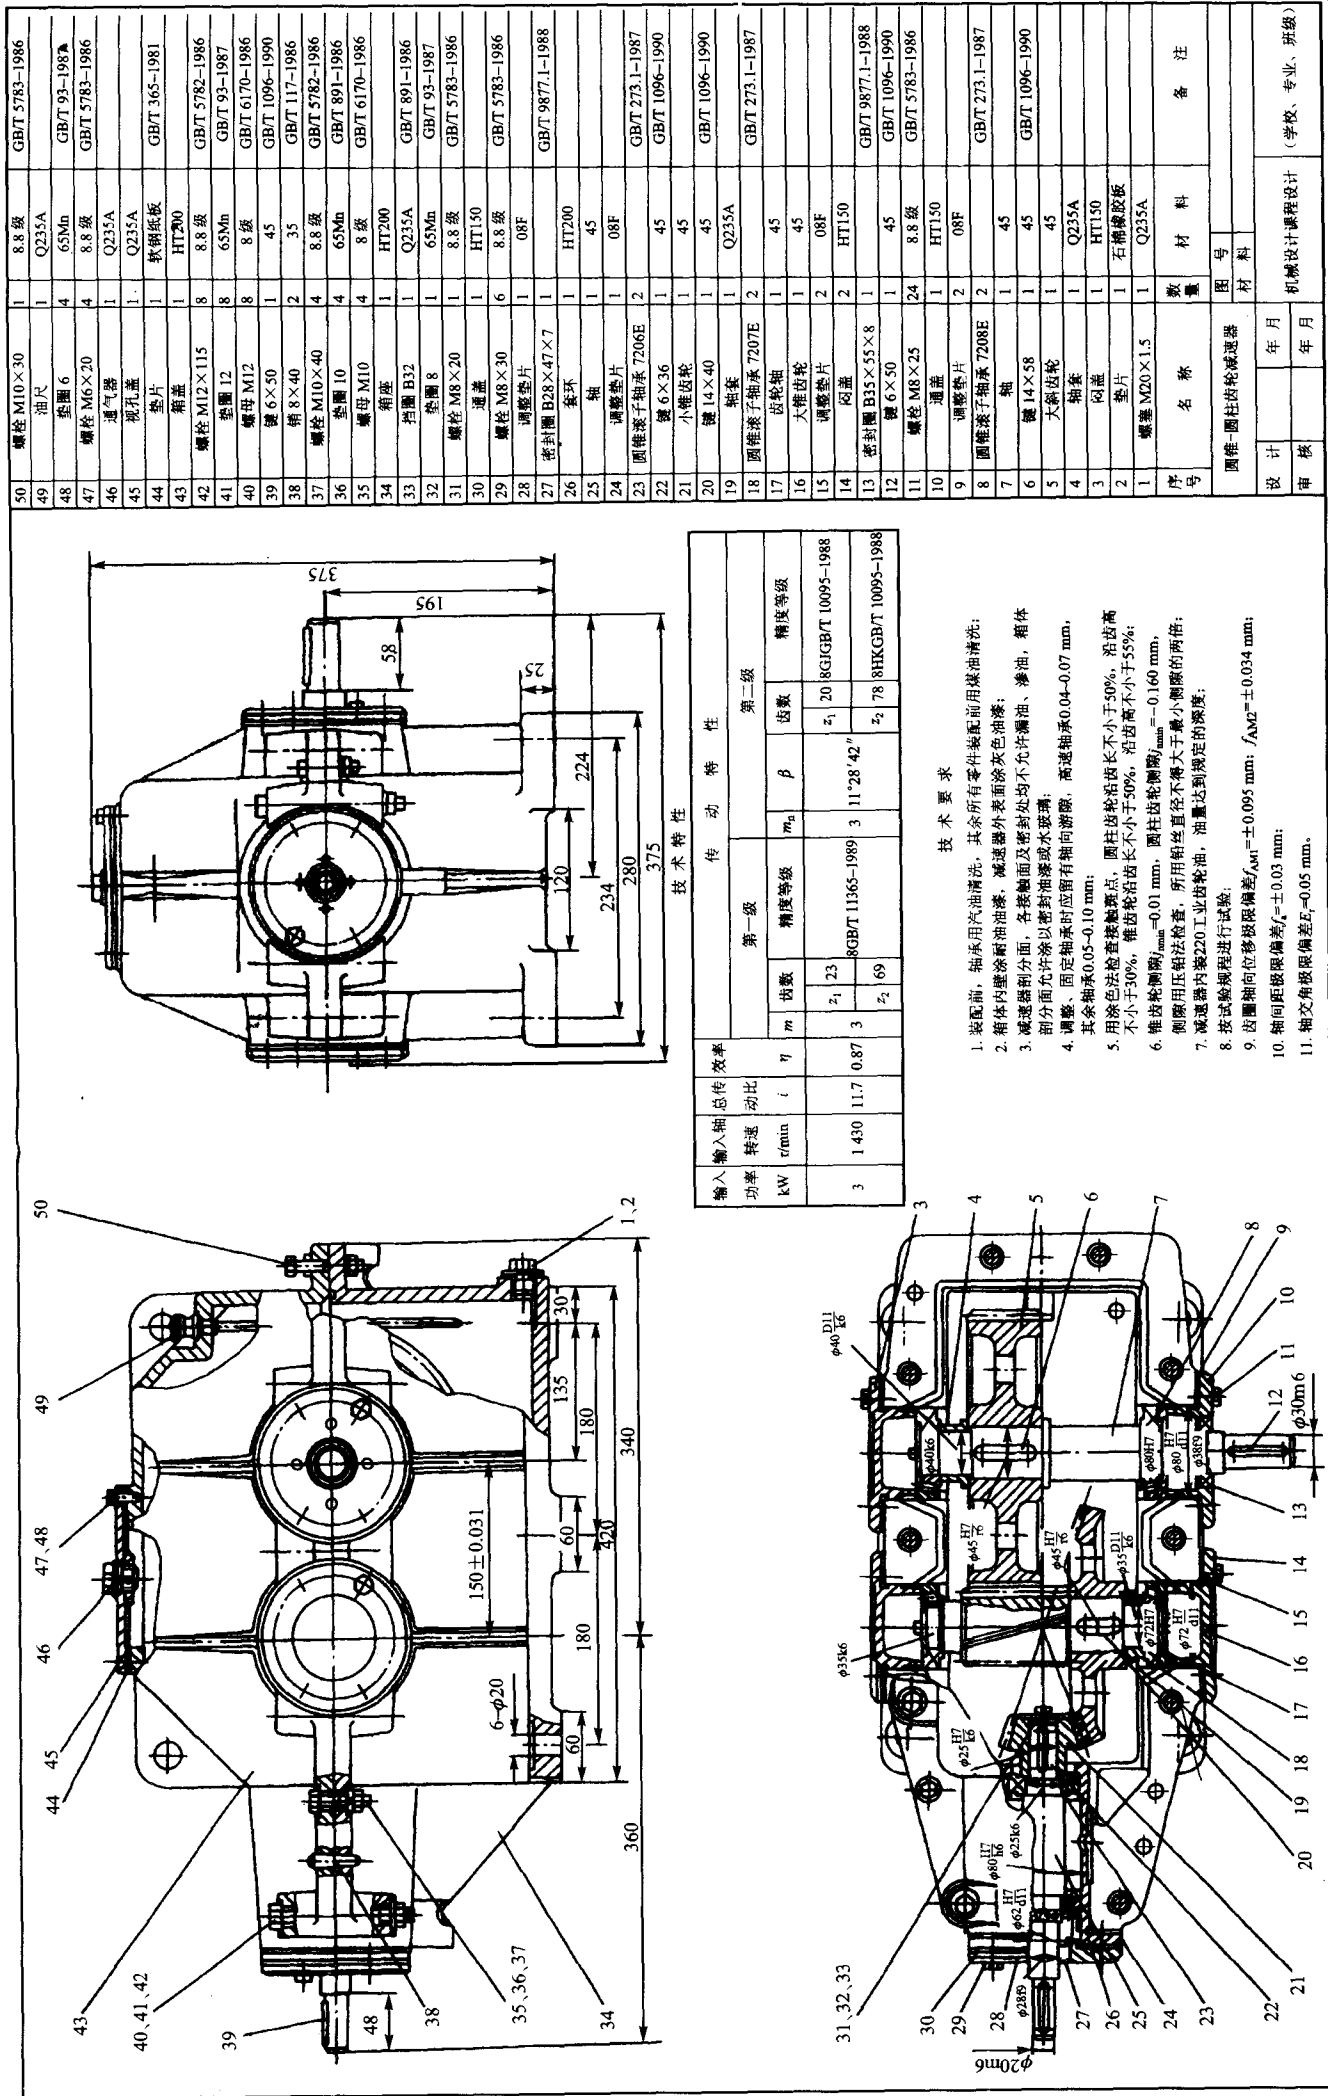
圆锥-圆柱齿轮减速器装配工作图 (二)
